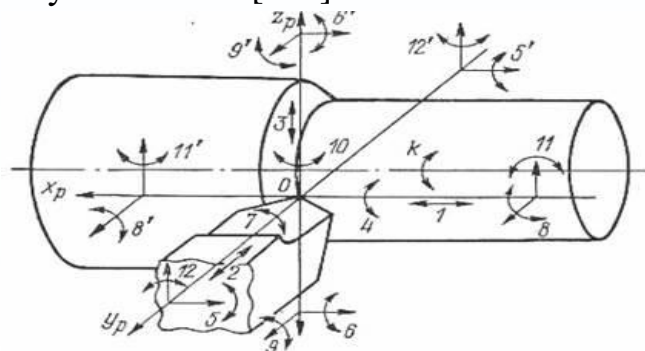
Схема напрямків відносних коливань інструменту і заготовки під час точіння [121]
